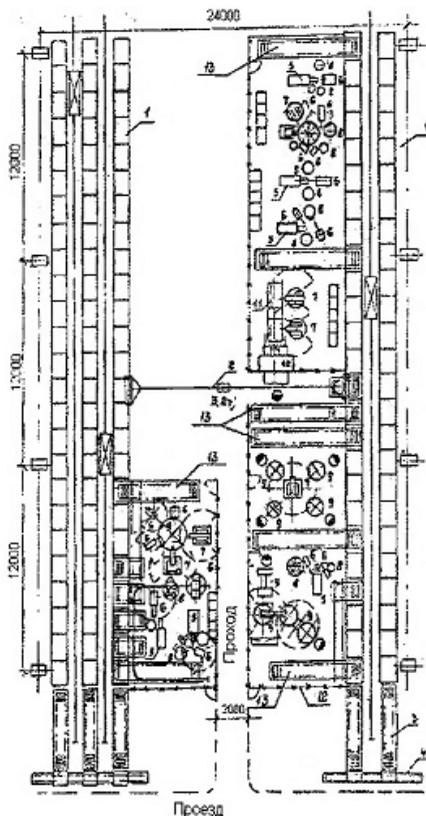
Гибкий автоматический участок сварки мелких узлов: 1 - высотный склад штамповок и узлов; 2 - кран - балка; 3 - рольганг; 4 - цепной конвейер; 5 - машина сварочная универсальная; 6 - робот промышленный для загрузки; 7 ~ робот для сварки; 8 - накопитель; 9 - стол поворотный для приспособлений; 10 - многоэлектродная машина; 11 - конвейер доварки; 12 - ограждение; 13 - подающее транспортное устройство.
